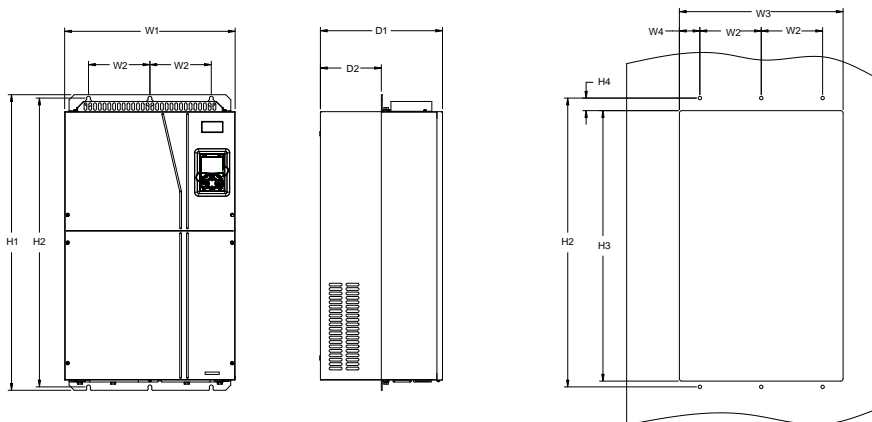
Схема ПЧ фланцевого монтажа 660 В, от 160 кВт до 220 кВт
